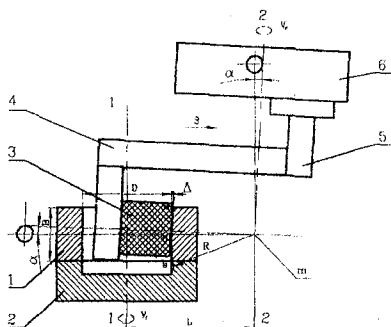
Схема способа формообразующего суперфиниширования деталей типа наружных колец роликоподшипников
